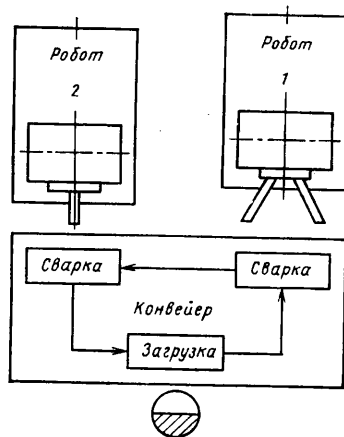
Автоматизированная линия сборки-сварки гнезда и крышки инструментального ящика
